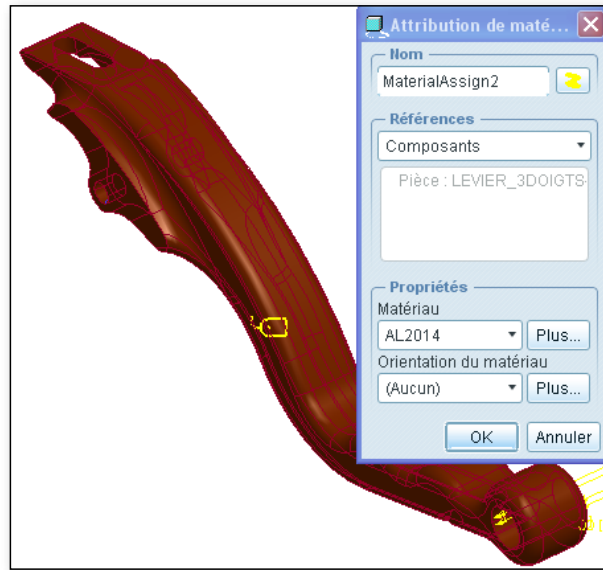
Levier de la poignée de frein de moto – Définition du matériau
